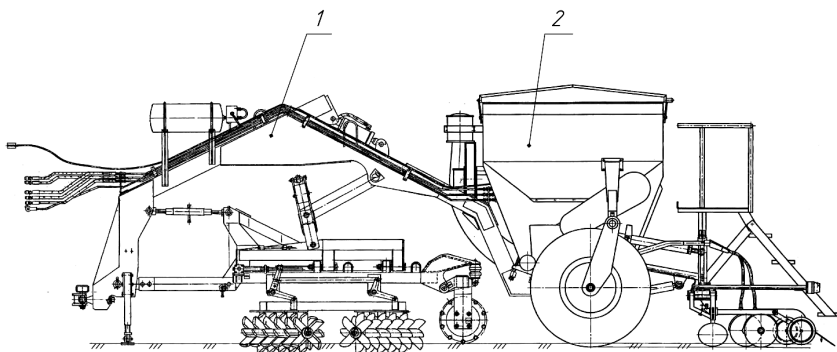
Схема почвообрабатывающего посевного агрегата АППА-4-02 с ножевидными рабочими органами (вид сбоку):
